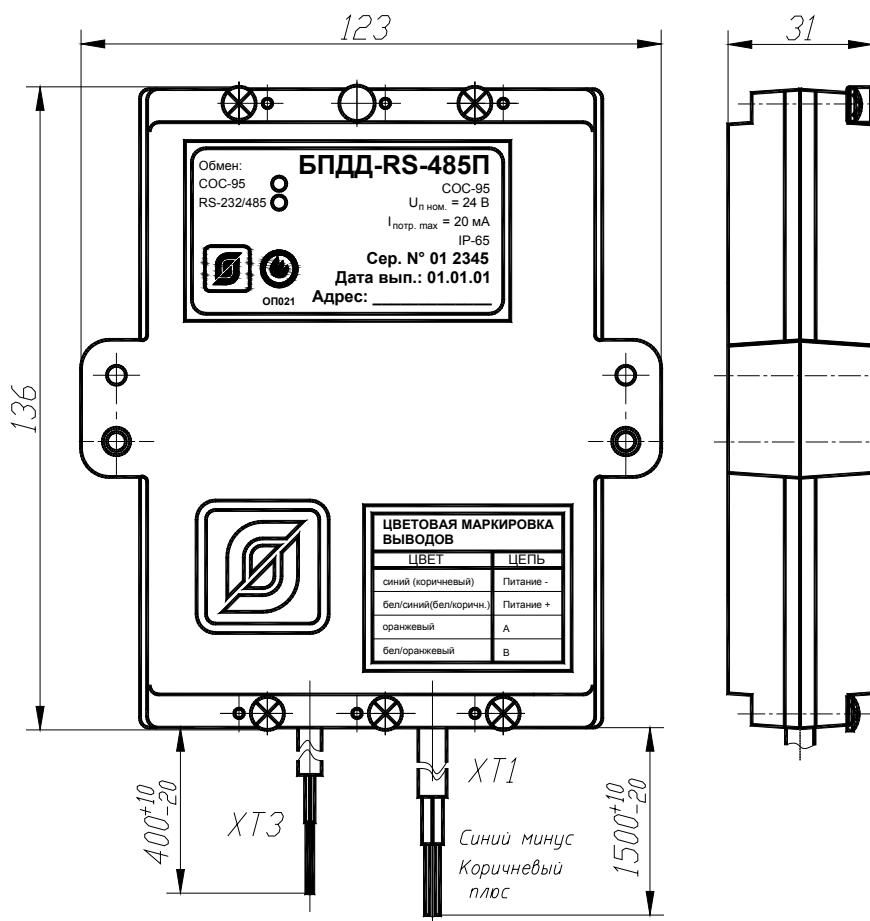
Габаритные размеры БПДД-RS-485П
